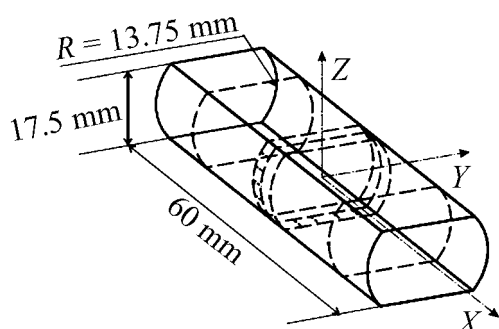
Схема и система координат обрабатываемой заготовки: направление оси  $X$  совпадает с направлением ВЭ, --- — линии реза
